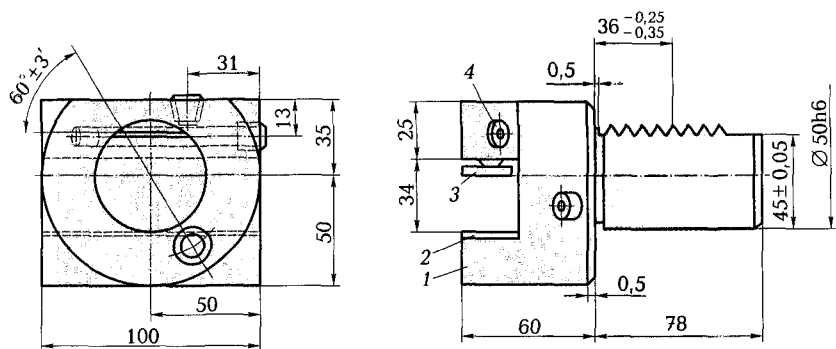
Резцедержатель с цилиндрическим хвостовиком:
